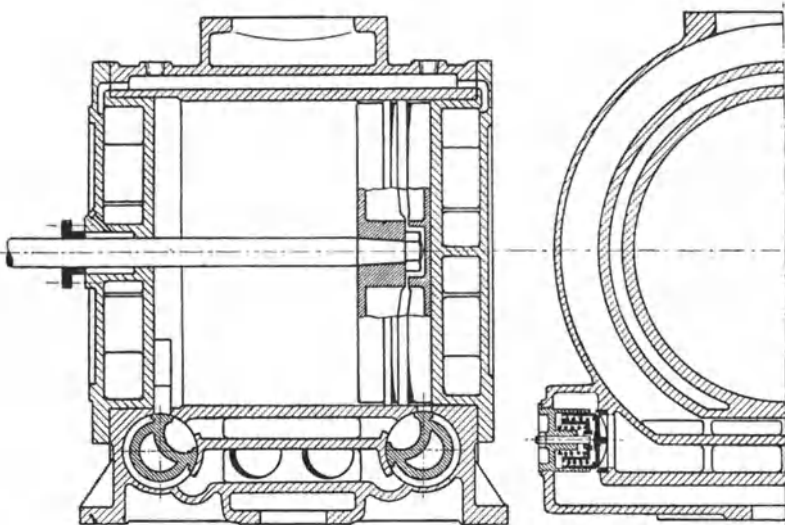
und 209. Kolben-Trockenluftpumpe ohne Druckausgleich der Wheeler Condenser and Engineering Co.
